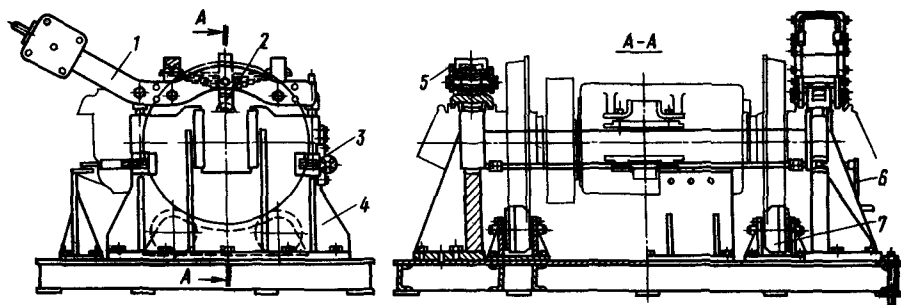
Стенд для обкатки колесно-моторного блока тепловоза:
